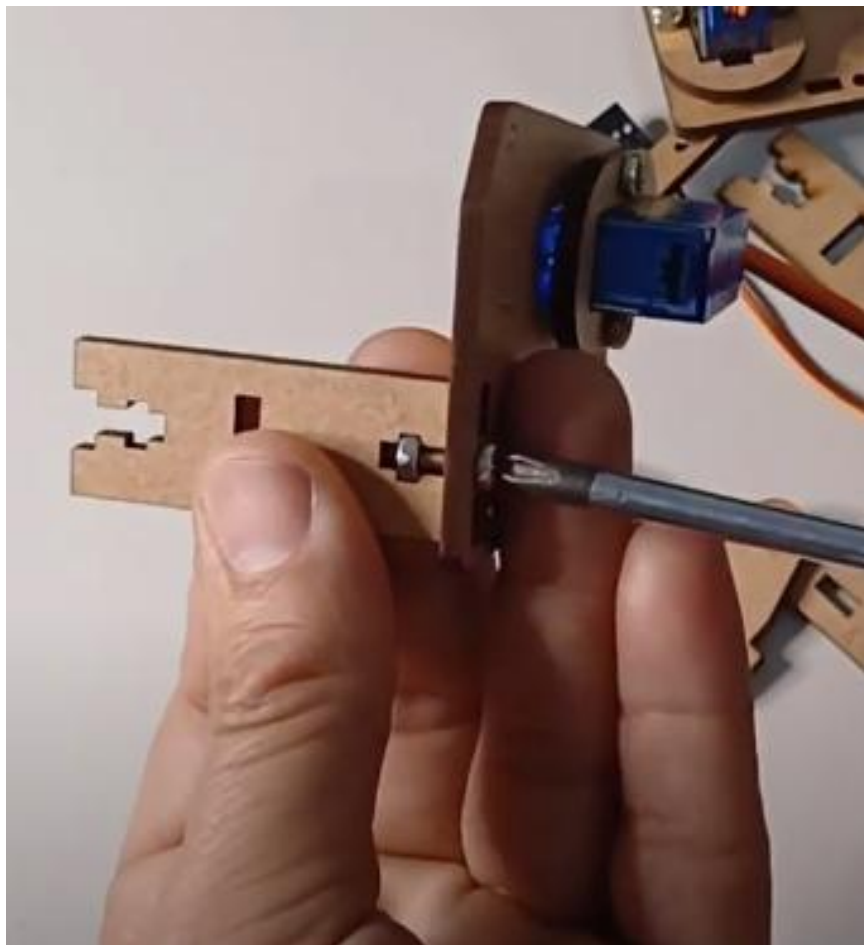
Montagem do Motor III, Suporte II e Montagem da Estrutura II - União das peças
